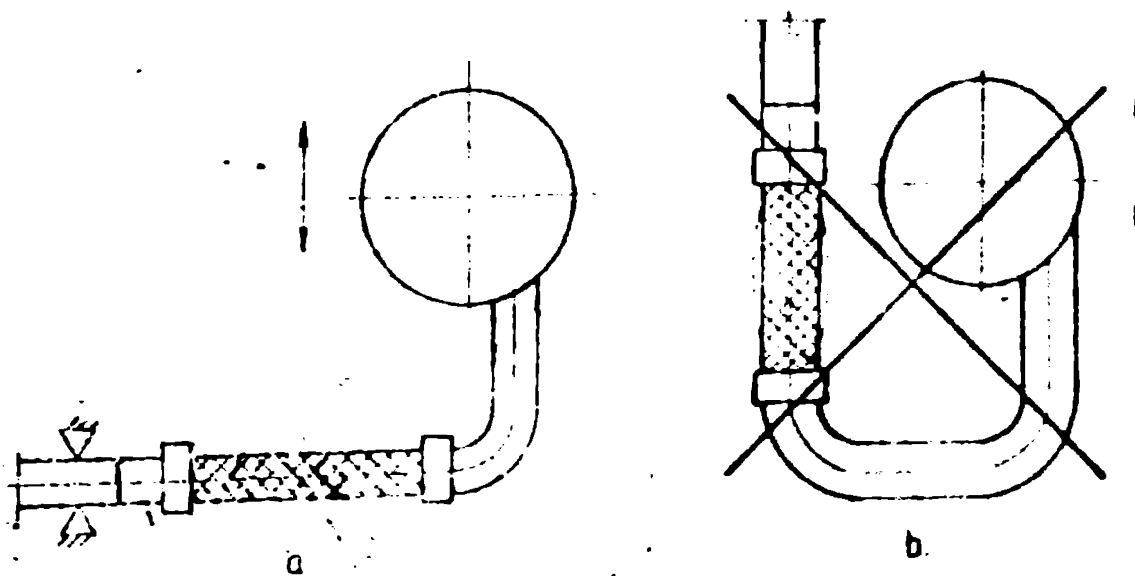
Montaj în unghi de 90° cu un singur tub flexibil.
